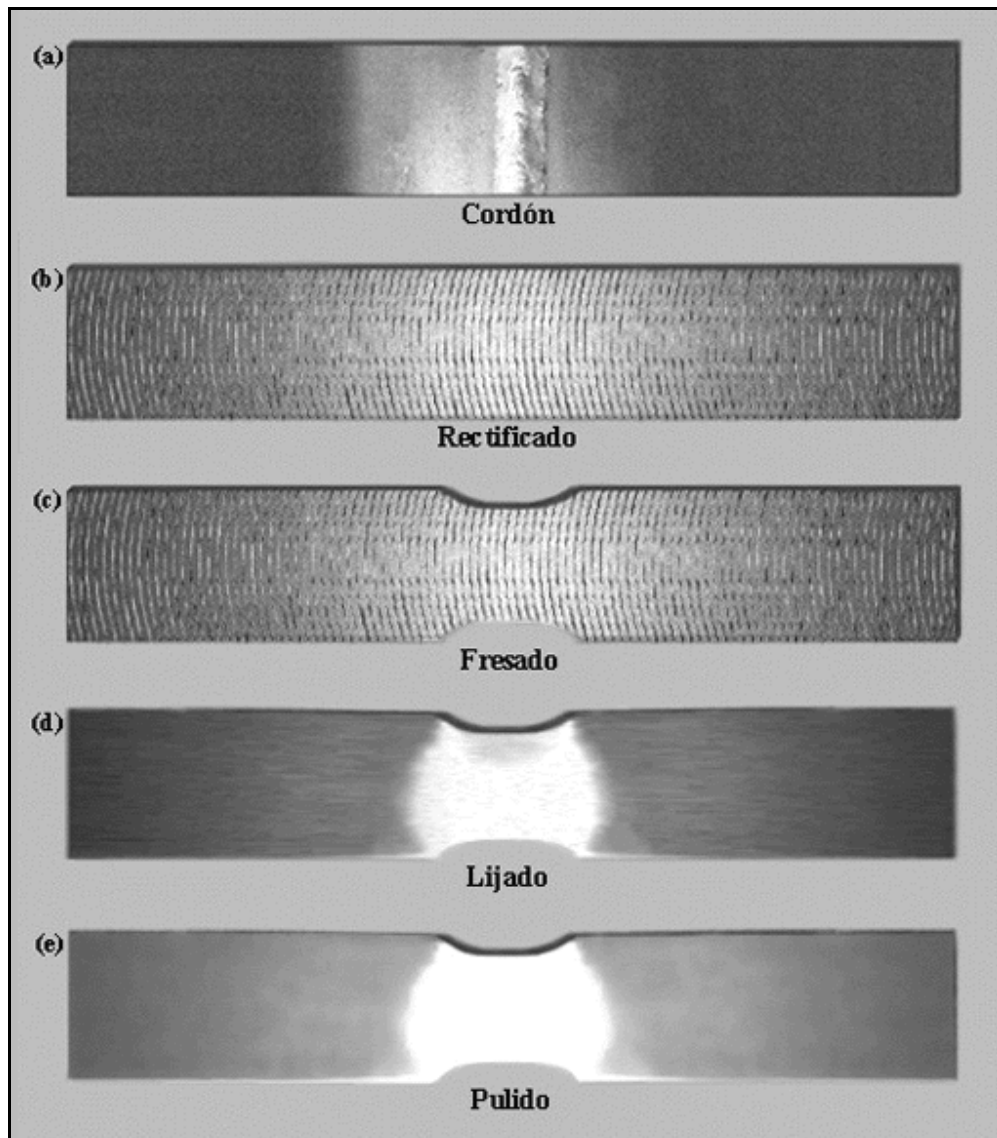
Pasos utilizados en la fabricación de las probetas para el ensayo de tracción de las juntas soldadas. (a) Cordón de soldadura; (b) Rectificado del cordón con una máquina para esmerilado plano; (c) Fresado de las probetas; (d) Lijado grueso con grano 80; (e) Lijado fino o pulido con grano 1500.
